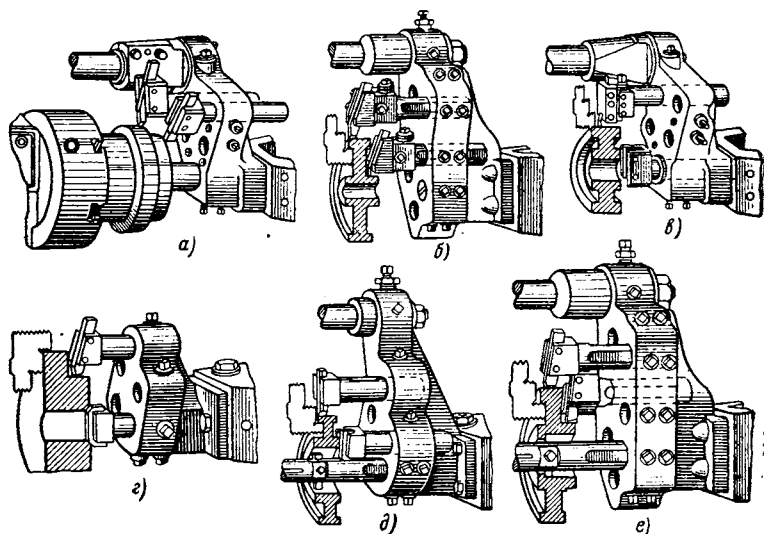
Приемы совмещения режущих инструментов при обработке деталей на станках с вертикальным расположением оси револьверной головки
